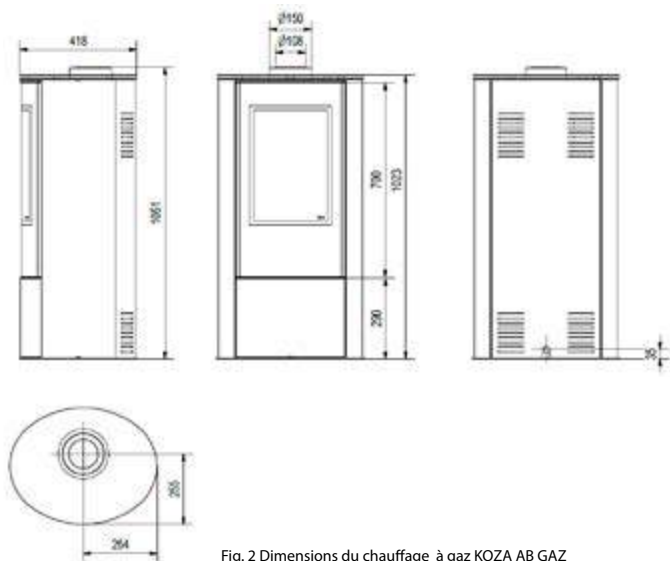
Dimensions du chauffage à gaz KOZA AB GAZ
